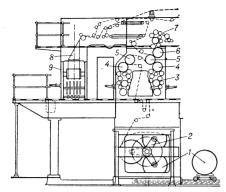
Схема секции газетного агрегата ГАУ: 1 — рулон бумаги; 2 — рулонная звезда; 3 — красочный аппарат основной краски; 4 — формный цилиндр основной краски; 5 — печатный цилиндр; 6 — формный цилиндр второй краски; 7 — красочный аппарат второй краски; 8 — воронка; 9 — фальцаппарат.
